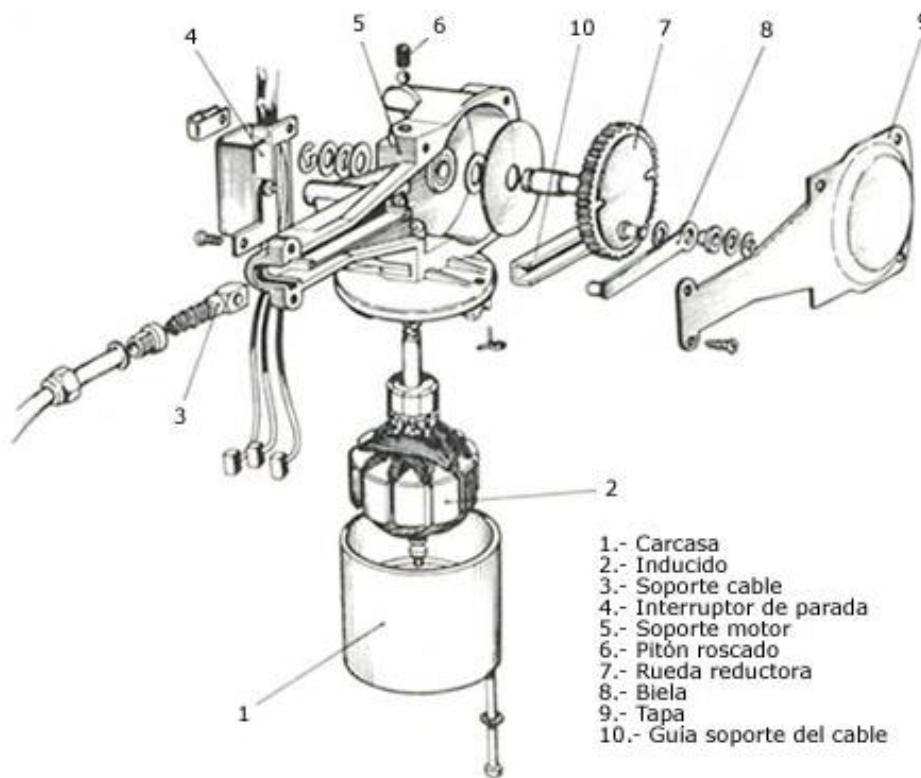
Motor con transmisión por cable flexible para limpiaparabrisas
